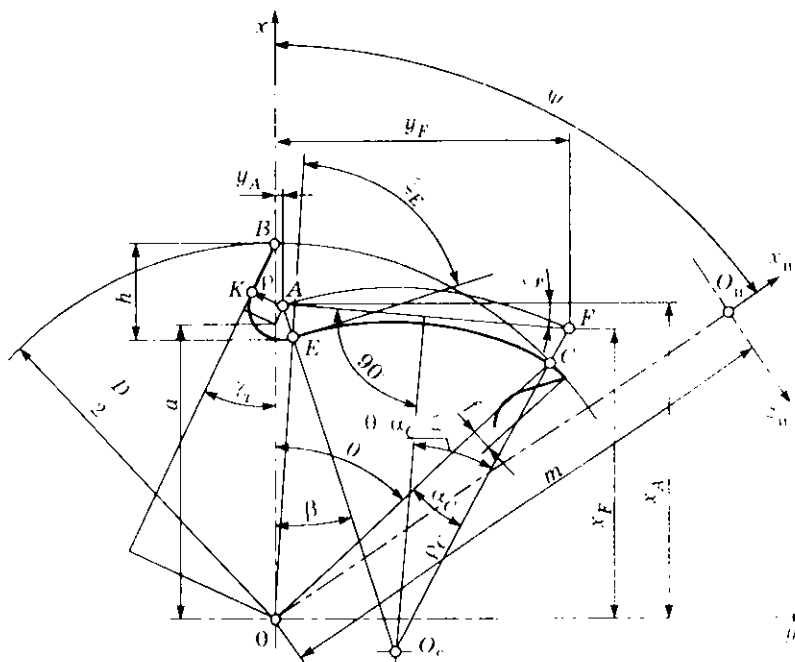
Схема определения параметров r , δ , ξ профиля стружечной канавки фрезы с параболической формой зуба
